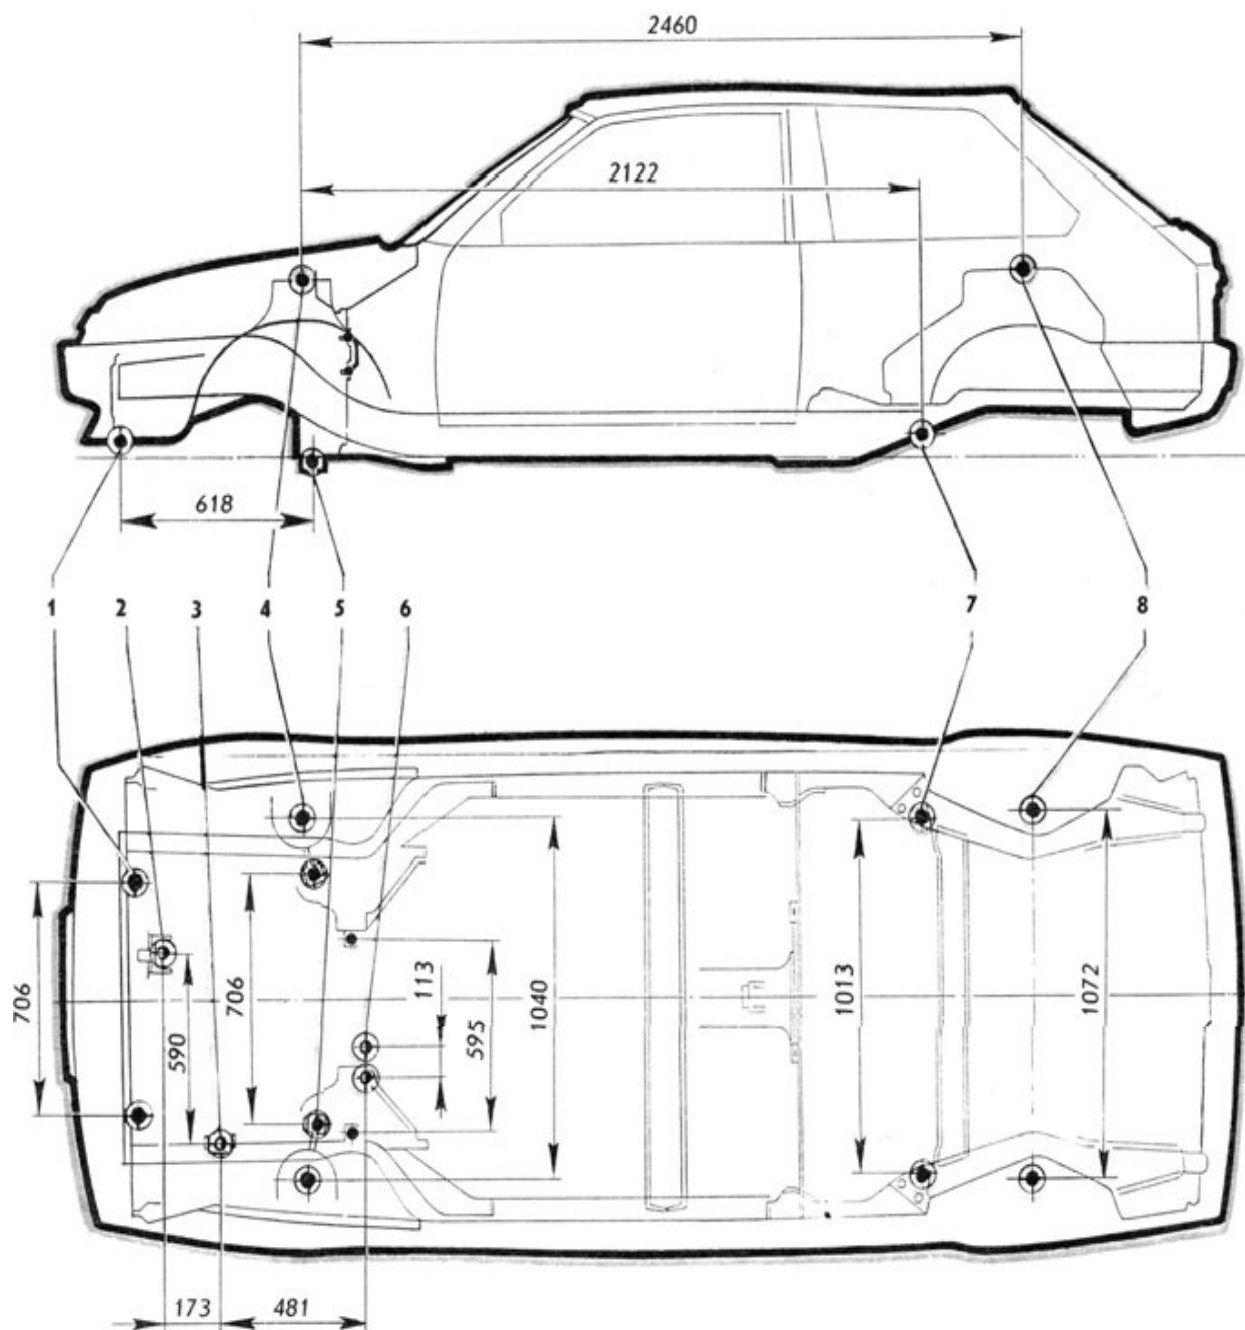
Точки крепления двигателя и подвесок на кузове автомобилей моделей ВАЗ-2108, ВАЗ-2109: 1 – растяжки передней подвески; 2 – передней опоры силового агрегата; 3 – левой опоры силового агрегата; 4 – верхнего шарнира стойки; 5 – шарнира рычага передней подвески; 6 – задней опоры силового агрегата; 7 – рычага задней подвески; 8 – амортизатора задней подвески.
